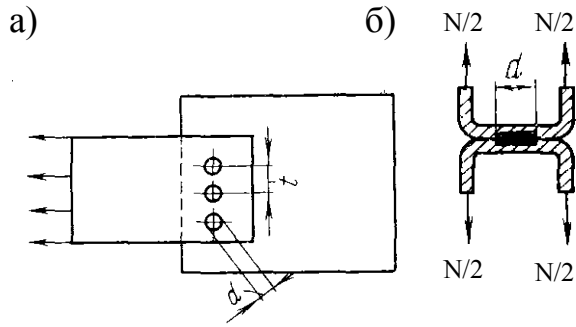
Схемы точечных сварных соединений:
